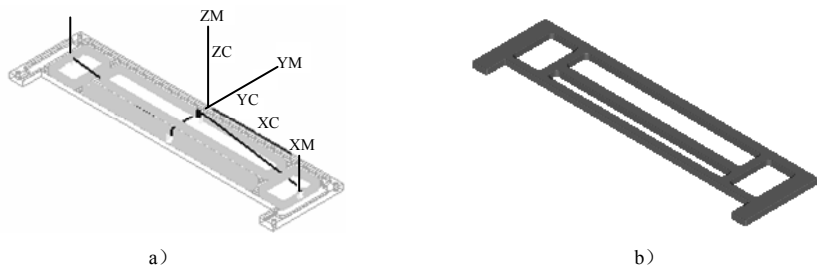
内腔平面铣精加工的“刀具路径”和“实体切削验证”
